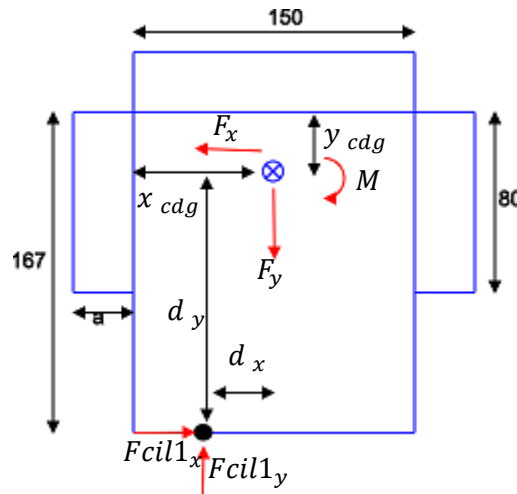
(1): Geometría de cordón de soldadura
